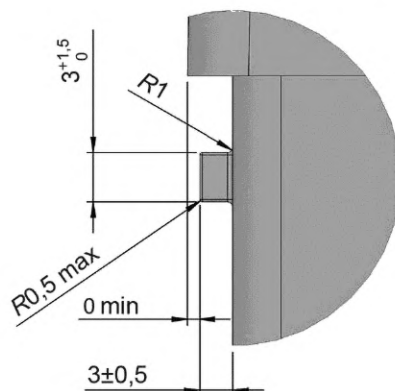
Форма и размеры выступа для ЗРО (деталь U), приведенного на рисунках 13 и 22
